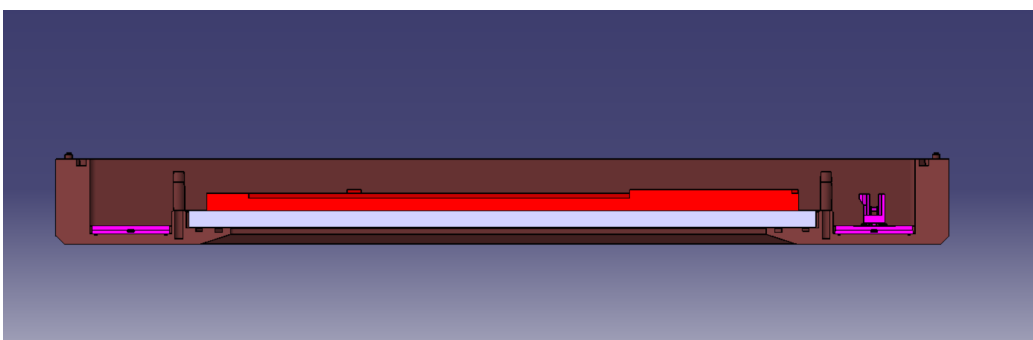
Sezione sul piano ZY dei componenti accoppiati al frame
